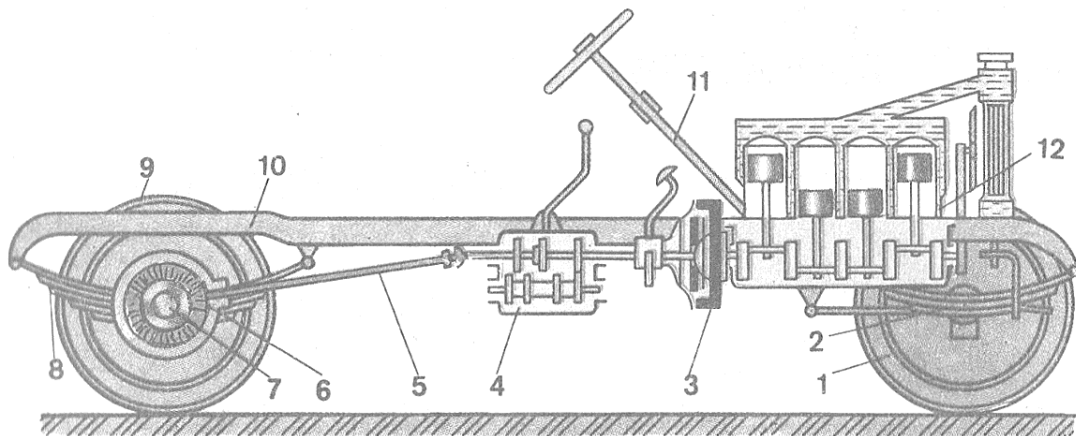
Розташування основних частин, їх механізмів і деталей автомобіля:
